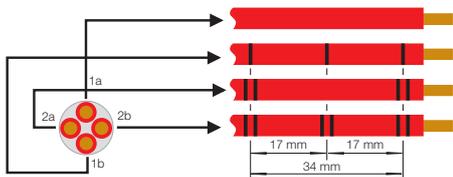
Sternvierer - Kennzeichnung mit Ringen
